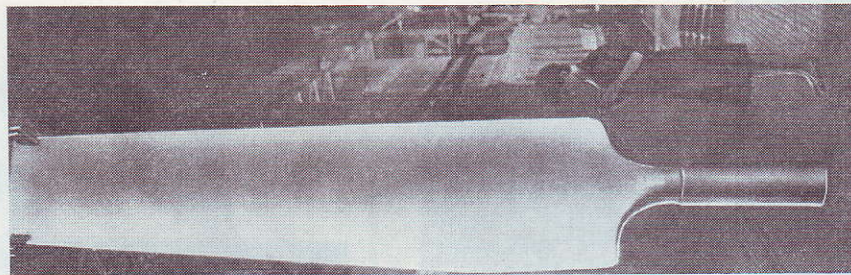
Штампованная поковка лопасти вентилятора градирни
